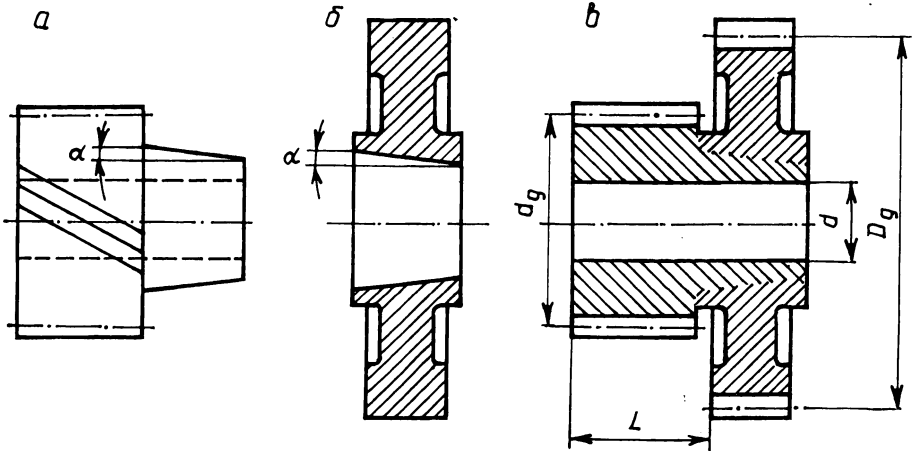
Схема получения блока шестерен методом холодной сварки:
